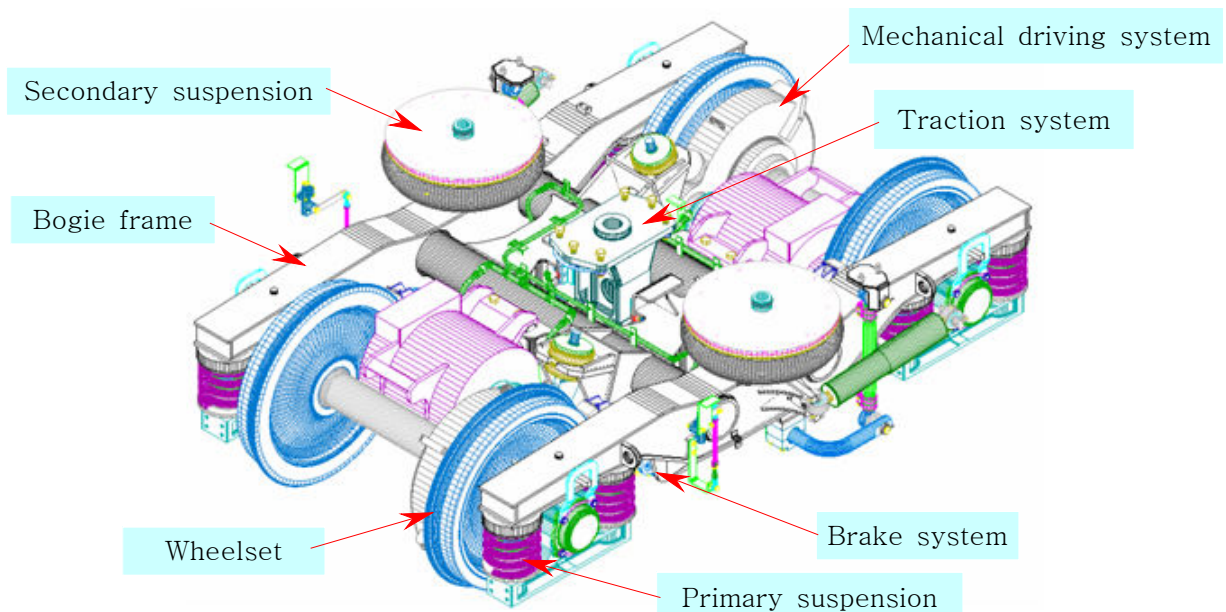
협궤용 준고속 개발 대차의 Isometric View
